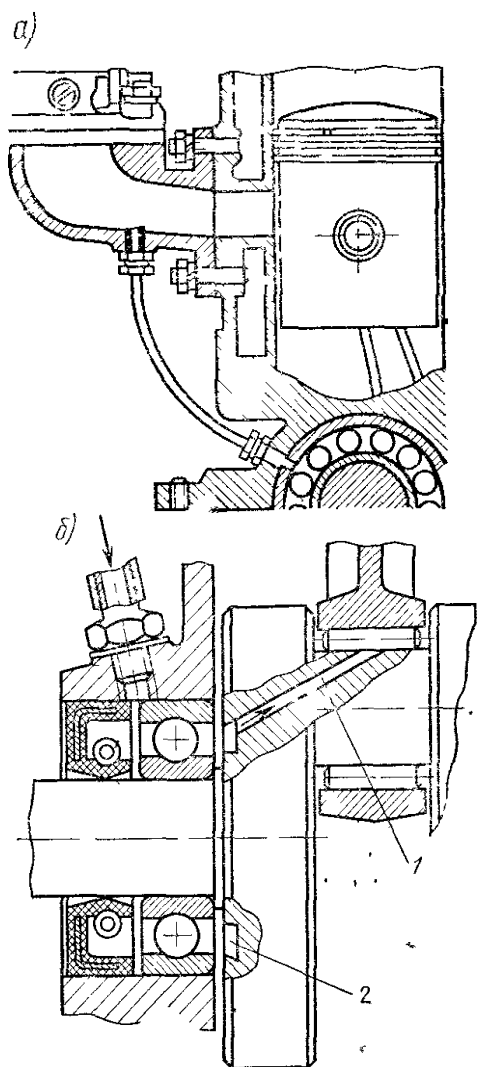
Смазка подшипников двухтактных двигателей с отбором масляной пленки из впускного трубопровода (а), с принудительной , подачей масла (б)
